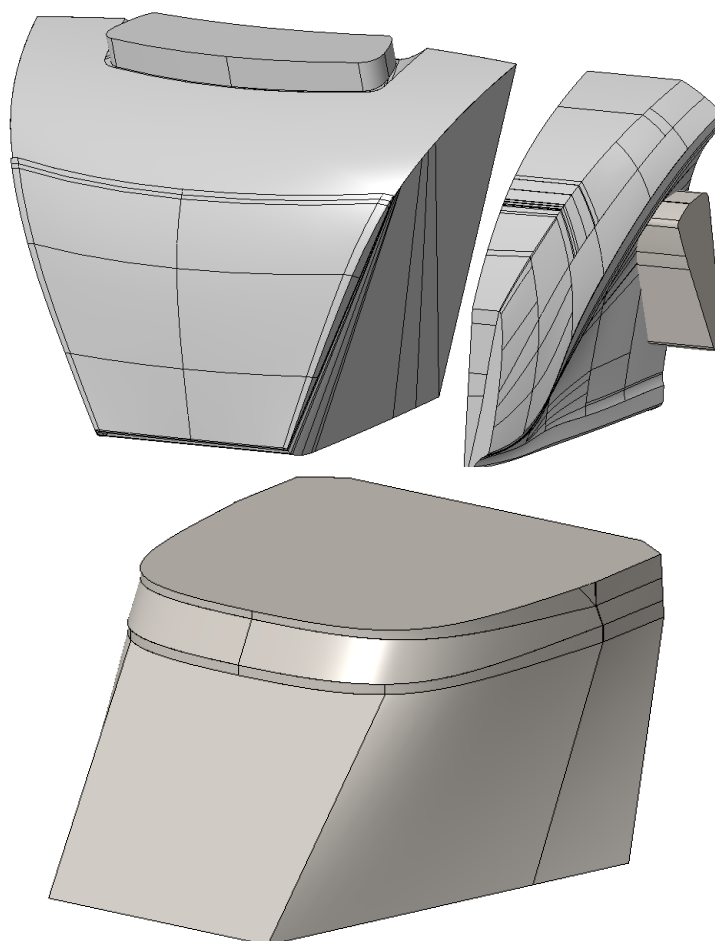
Uzavřená karoserie a zjednodušené díly prostoru chladiče
